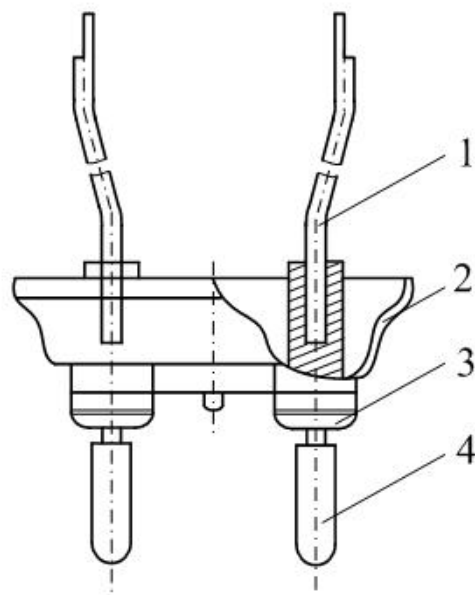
Конструкція вузла ніжки і цоколя типу „Біпост G-38” 1 – струмоввід; 2 – скляна ніжка; 3 – коваровий ковпачок для „ножового” з’юста зі склом; 4 – масивний мідний шпиль.
